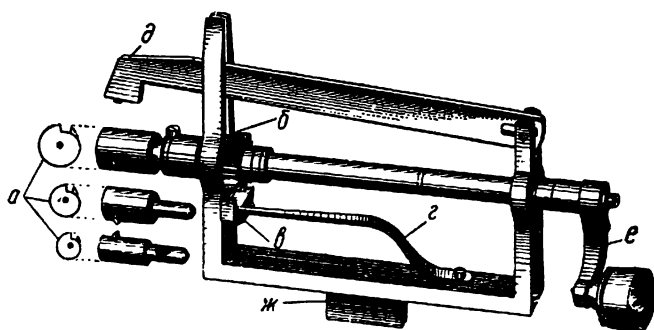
Машинка для завивки пружин: а — вставные центры для завивки пружин с правыми и левыми крючками; б — храповое колесо; в — двусторонняя собачка; г — пружинка, передвигаемая при перестановке собачки; д — рычаг с крючком для замка пружины; е — вал с ручкой; ж — место крепления машинки в тисках
